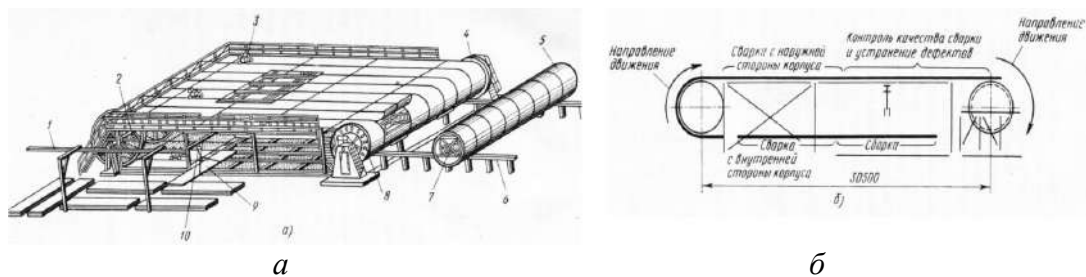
Изготовление негабаритных резервуаров рулонированием:
